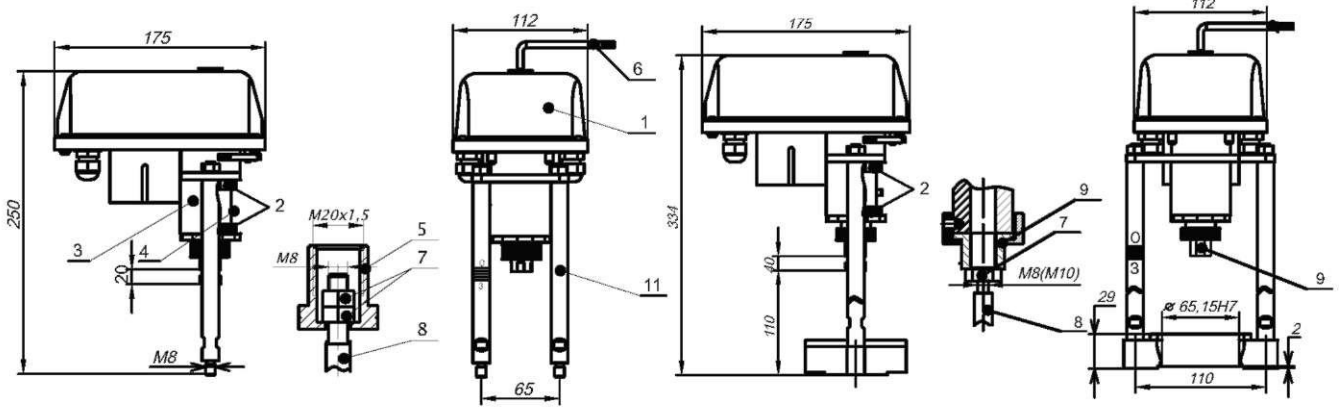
ВЭП-05-3000, ВЭП-15-3000, ВЭП-25-3000
